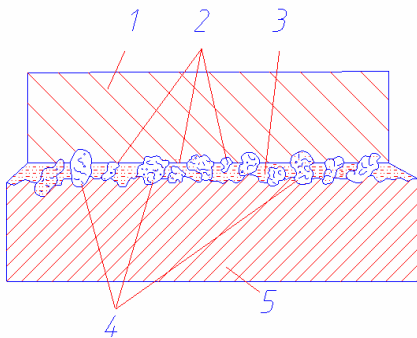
Доводка при помощи абразивов: 1 – притир; 2 – осколки абразивных зерен; 3 – смазочно-охлаждающая жидкость; 4 – абразивные зёрна; 5 – обрабатываемая поверхность детали
